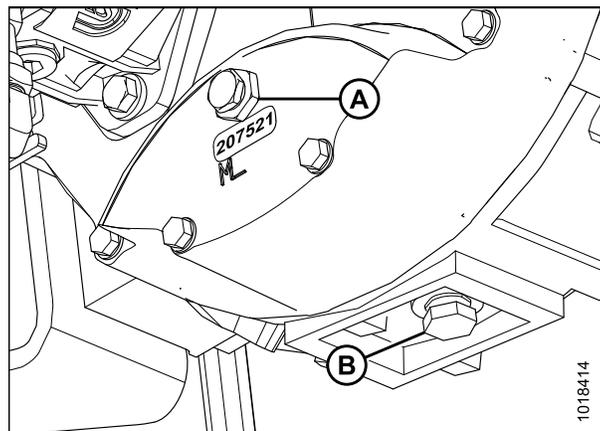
Пробка отверстия для слива масла из редуктора
